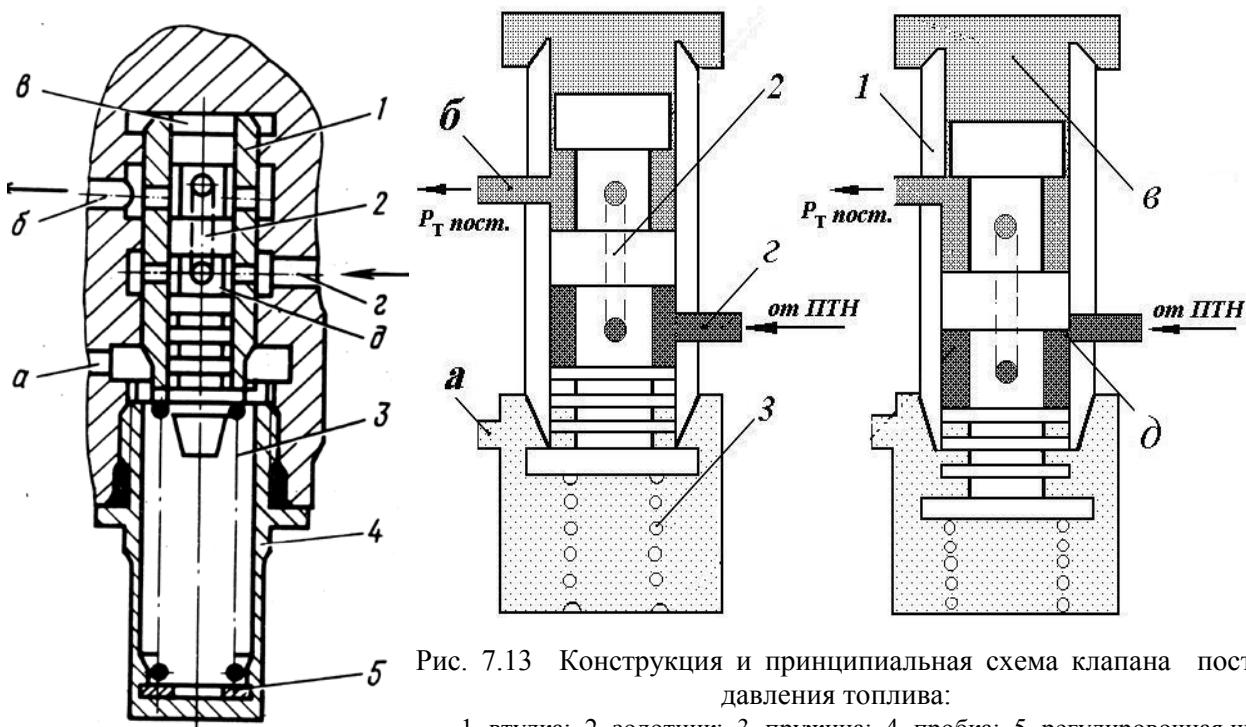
Конструкция и принципиальная схема клапана постоянного давления топлива:
